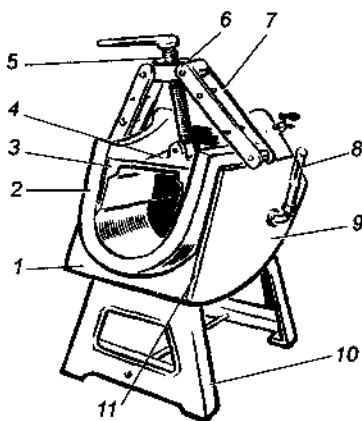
Секторная форма-мульда: 1 — корпус; 2 — паровая рубашка; 3 — бортовые вкладыши; 4 — подпятник; 5 — нажимный винт; 6 — траверса струбины; 7 — струбина; 8 — термометр; 9 — щиток; 10 — чугунная подставка; 11 — асбест для теплоизоляции корпуса мульды
